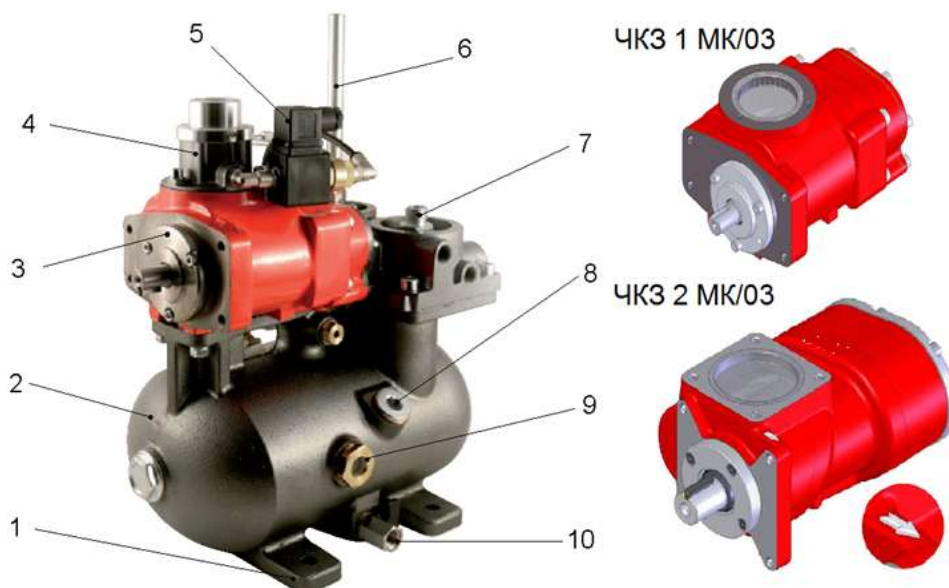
Модули компактные компрессорные: 1 – лапа; 2 – корпус сепаратора; 3 – компрессор; 4 – клапан впускной; 5 – электрокатушка; 6 – ниппель крепления сепаратора-ловушки; 7 – штуцер крепления фильма масляного; 8 – горловина маслonaливная; 9 – смотровое окно для наблюдения за уровнем масла; 10 – место под кран для слива масла.
